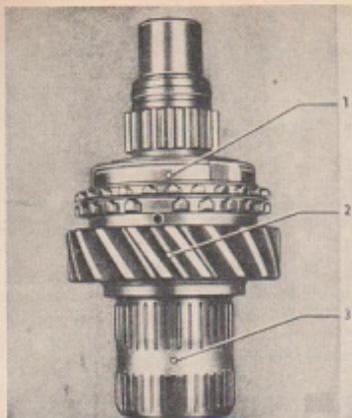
3. Gang-Zahnrad mit Synchronring auf Hauptwelle aufgeschoben
